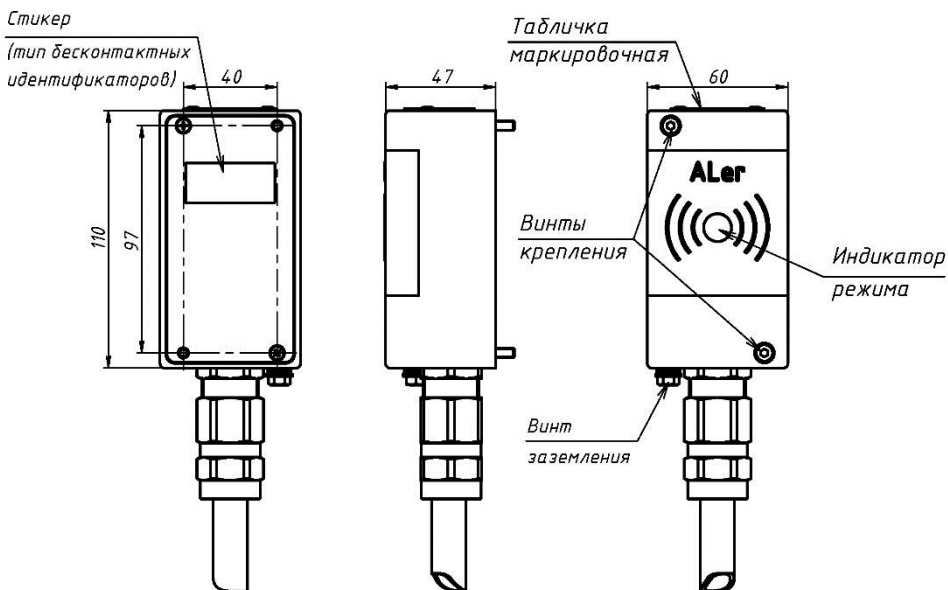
Габаритно-установочные размеры считывателя AL-RD-S04-NRU
